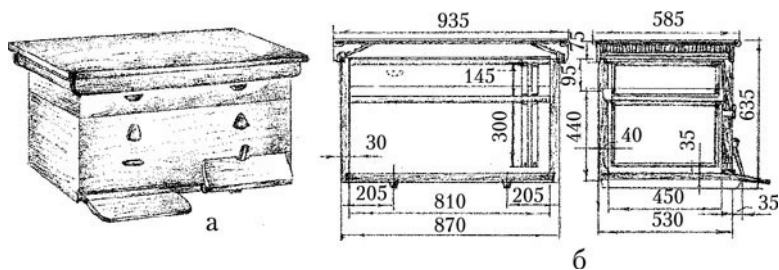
Улей-лежак: а – общий вид; б – устройство улья
